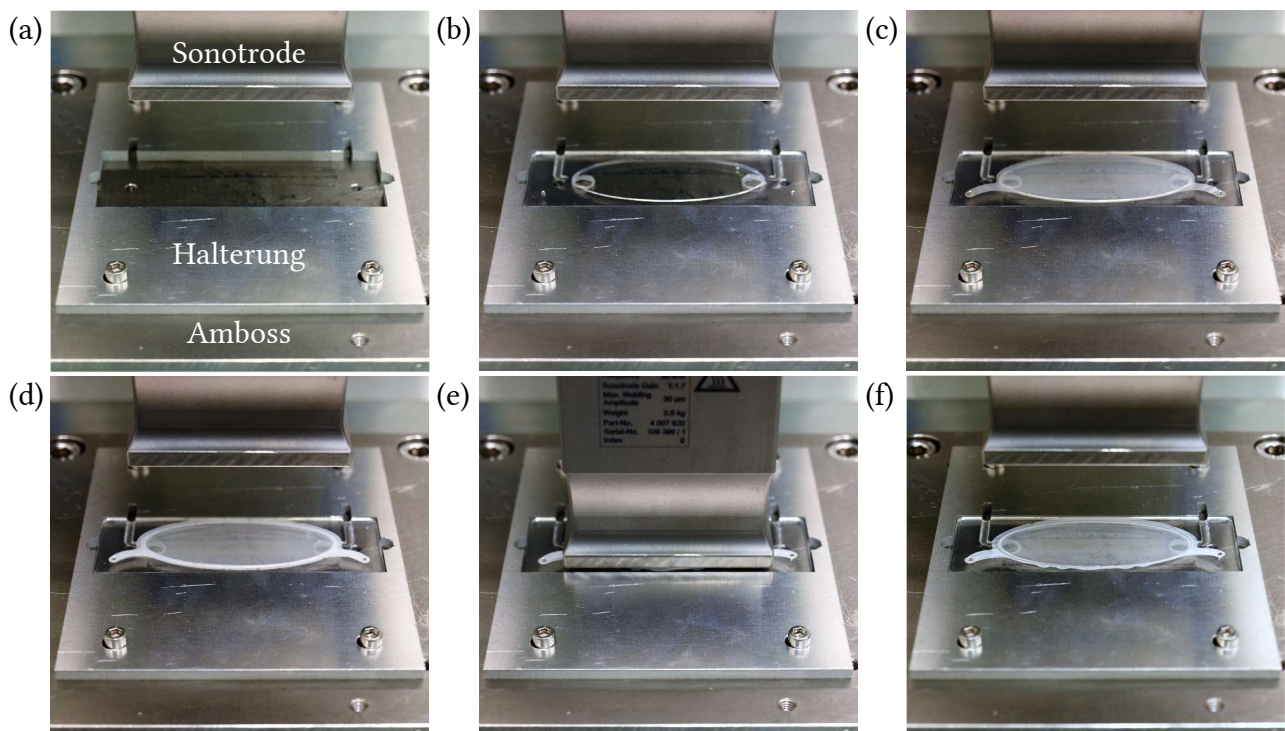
Schritte zum Ultraschallschweißen der Membranen mit dem PET-Gewebering auf die Chiphälfte mit Zellkammer, hier am Beispiel des 800 µl-MBR. (a) Ausrichten der Halterung auf dem Amboss, (b) Einlegen der Chiphälfte mit Zellkammer und Vorprägen, (c) Einlegen von Membran, (d) Eingelegen von PET-Gewebering, (e) Ultraschallschweißen aller Komponenten, (f) Chiphälfte mit aufgeschweißter Membran.
